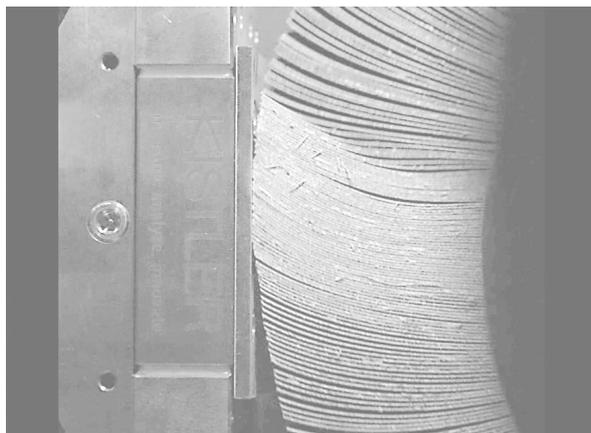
Контакт лепесткового круга с обрабатываемой поверхностью
